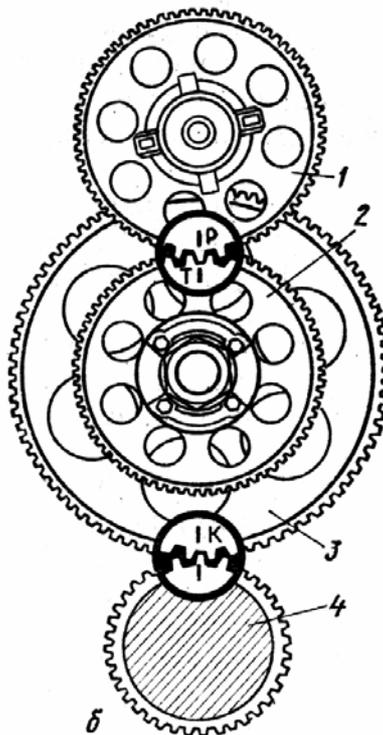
Газораспределительный механизм двигателя СМД-62:
